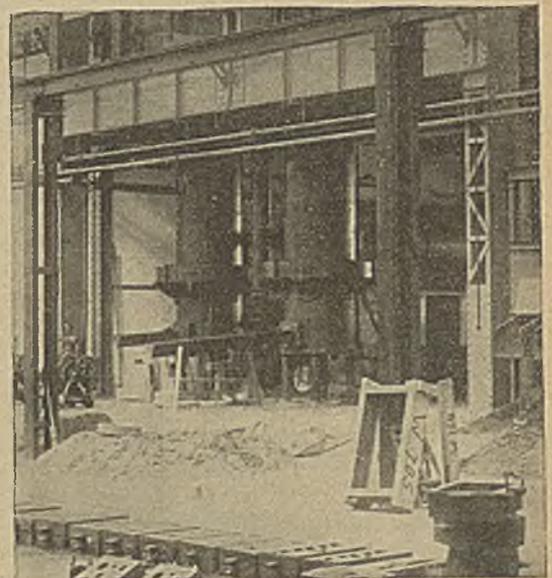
Ansicht der zwei Kuppelöfen mit gemeinsamer Funkenkammer.
